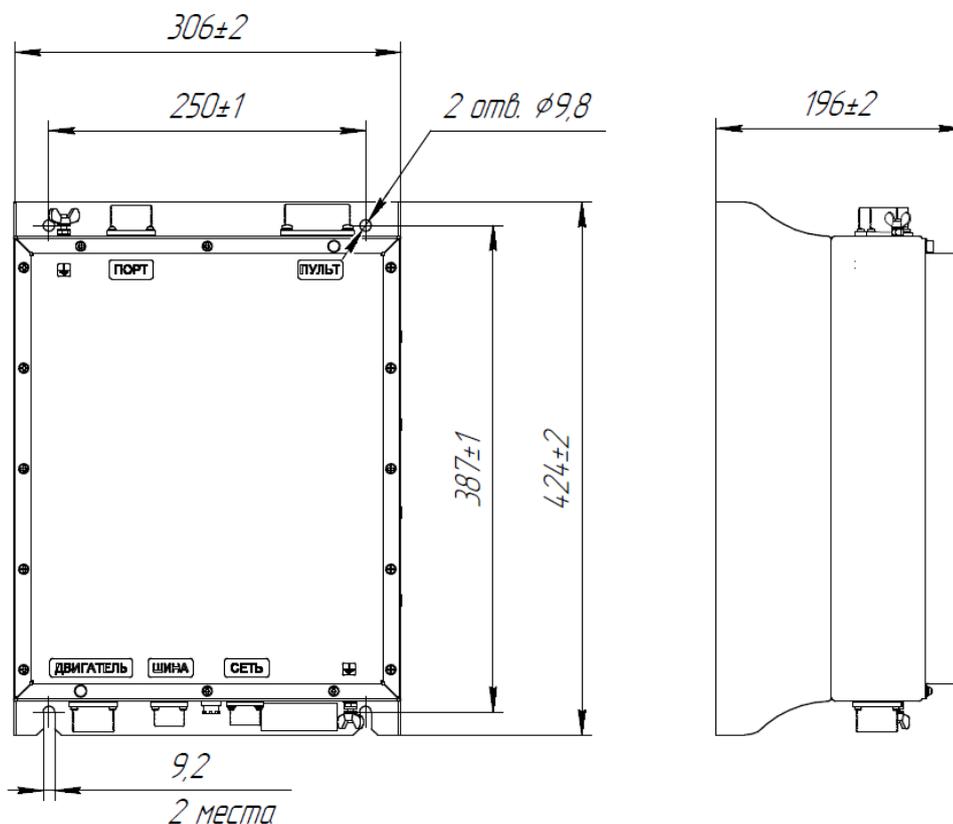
Внешний вид МПЧ-380-3,0-04
